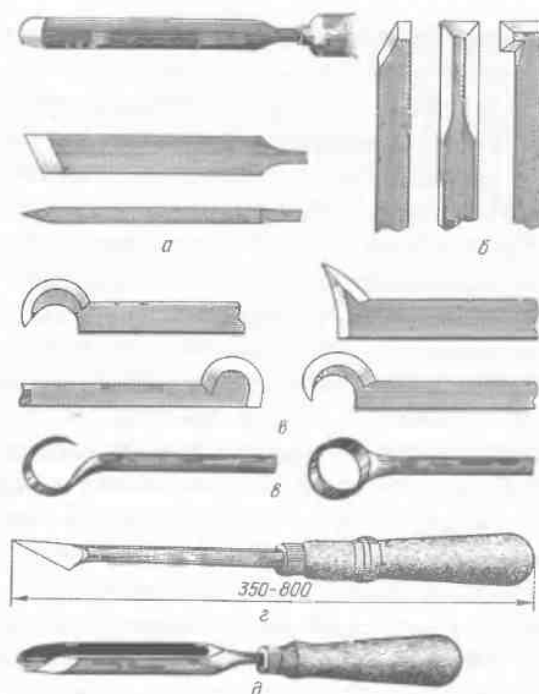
Инструменты для точения на токарном станке: а — приспособленная полукруглая стамеска для первичной обработки ровных поверхностей вращения и стамеска-косяк для чистовой обработки; б — инструмент для расточки углублений; в — крючки или выточки для цилиндрических или криволинейных внутренних поверхностей; г — универсальная стамеска-косяк для чистовой обработки, подрезки торцов и отрезания (острым концом), для получения канавок (пяткой); д — стамеска-трубка со спирально расположенным лезвием или со скошенными кромками (расширяет возможности полукруглой стамески)
